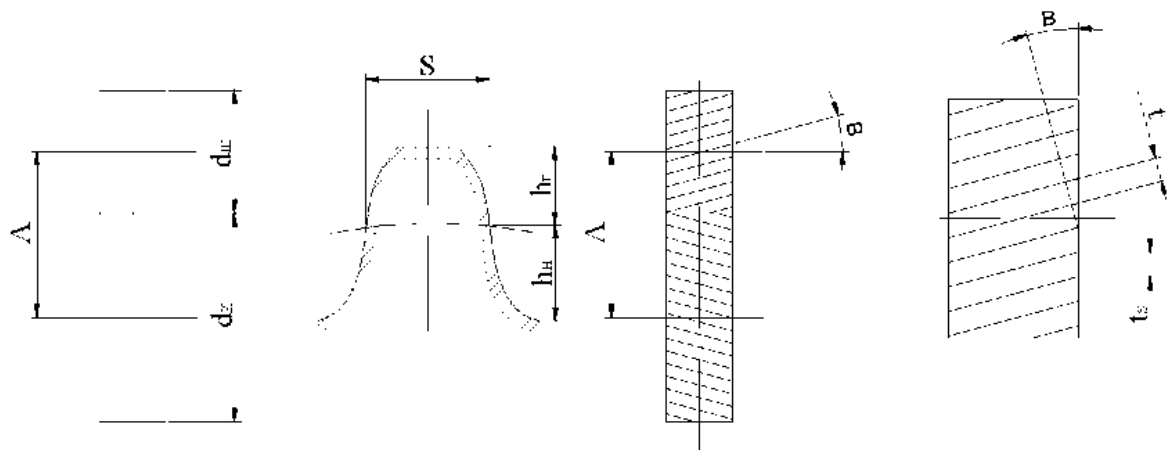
Прямозубые и косозубые цилиндрические шестерни
